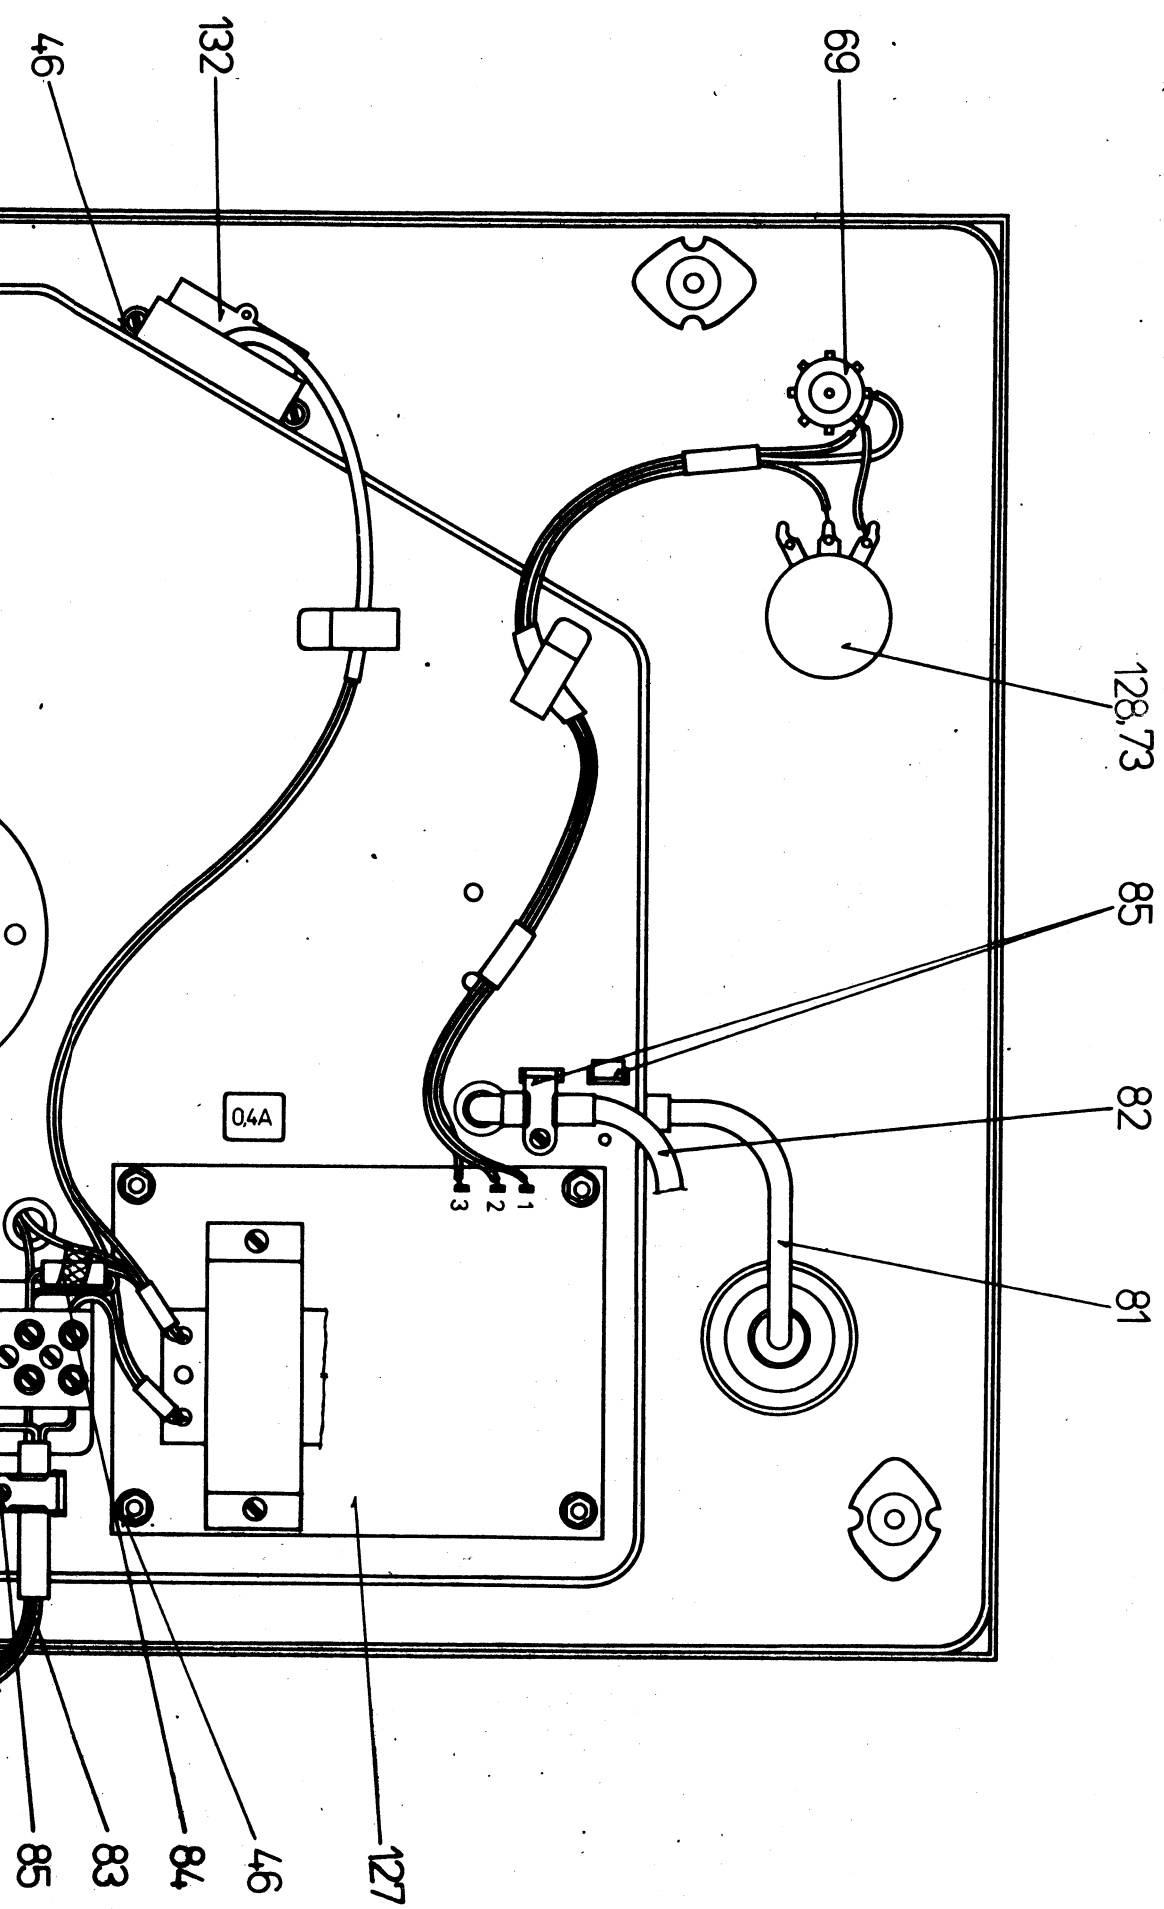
Náhradní a mechanické díly chassis - pohled shora
